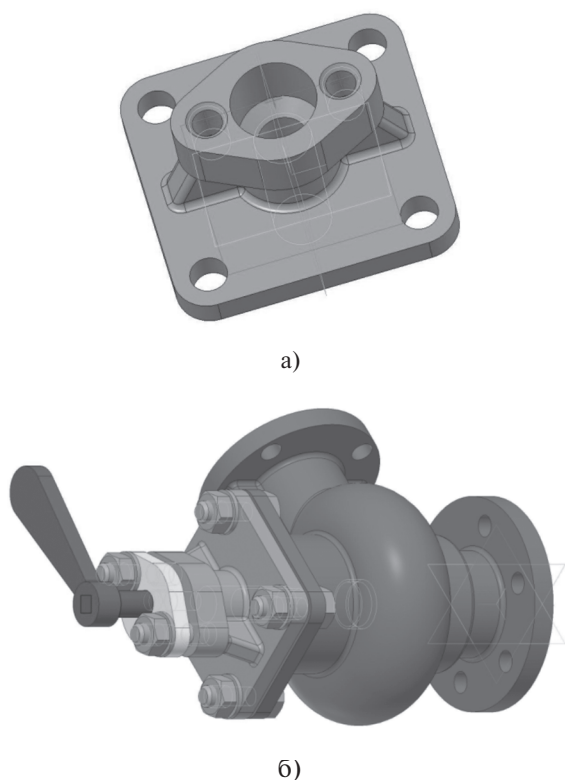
а) 3D-модель крышки вентиля запорного; б) 3D-модель вентиля запорного
